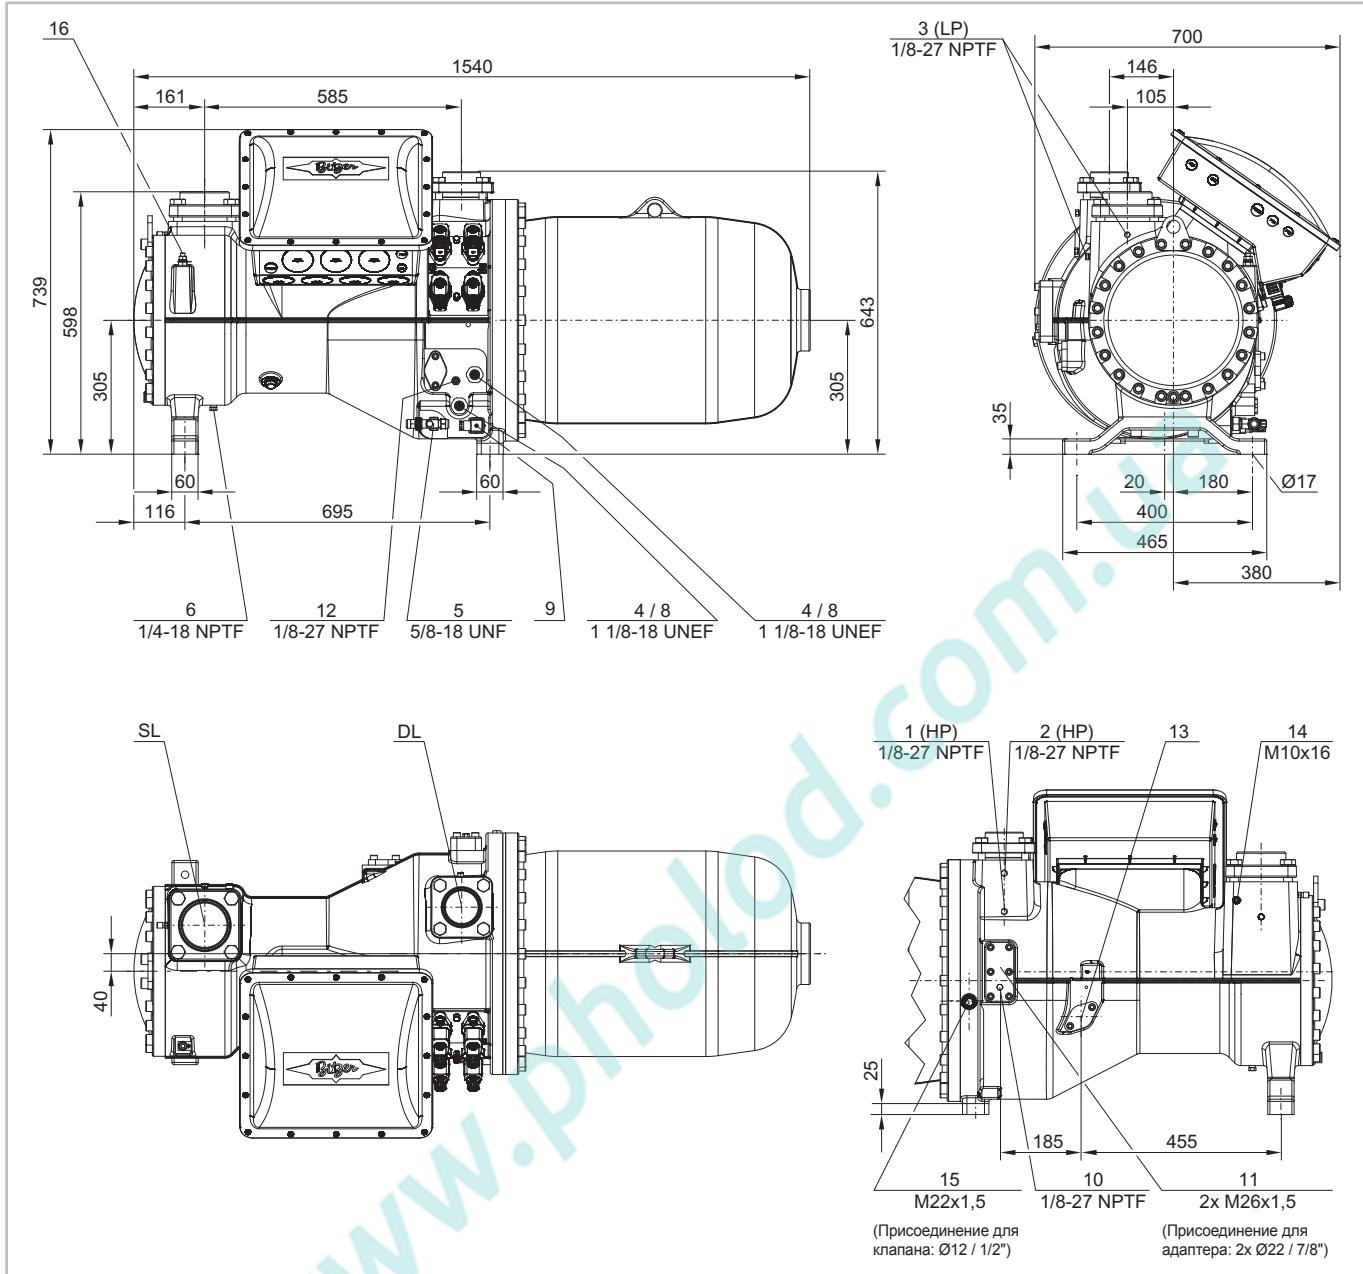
Чертежи с указанием размеров для компрессоров CSH8553-80Y .. CSH8593-180(Y)
